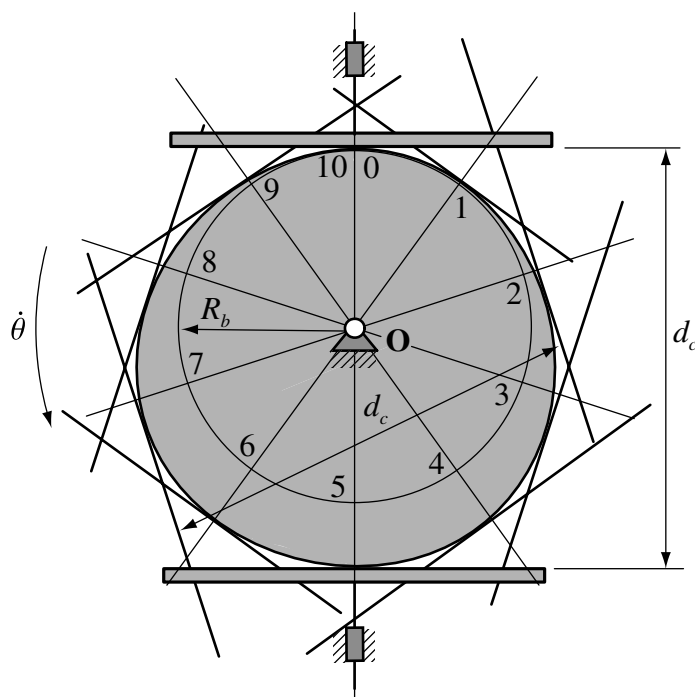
Obtención del perfil de leva de anchura constante con doble palpador plano de translación
